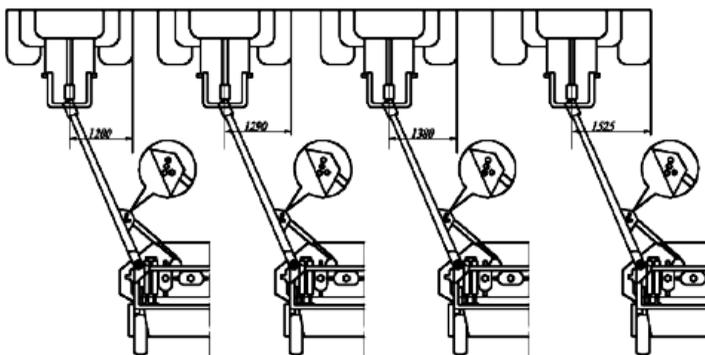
Схема корректировки бокового смещения дышла прицепного устройства
